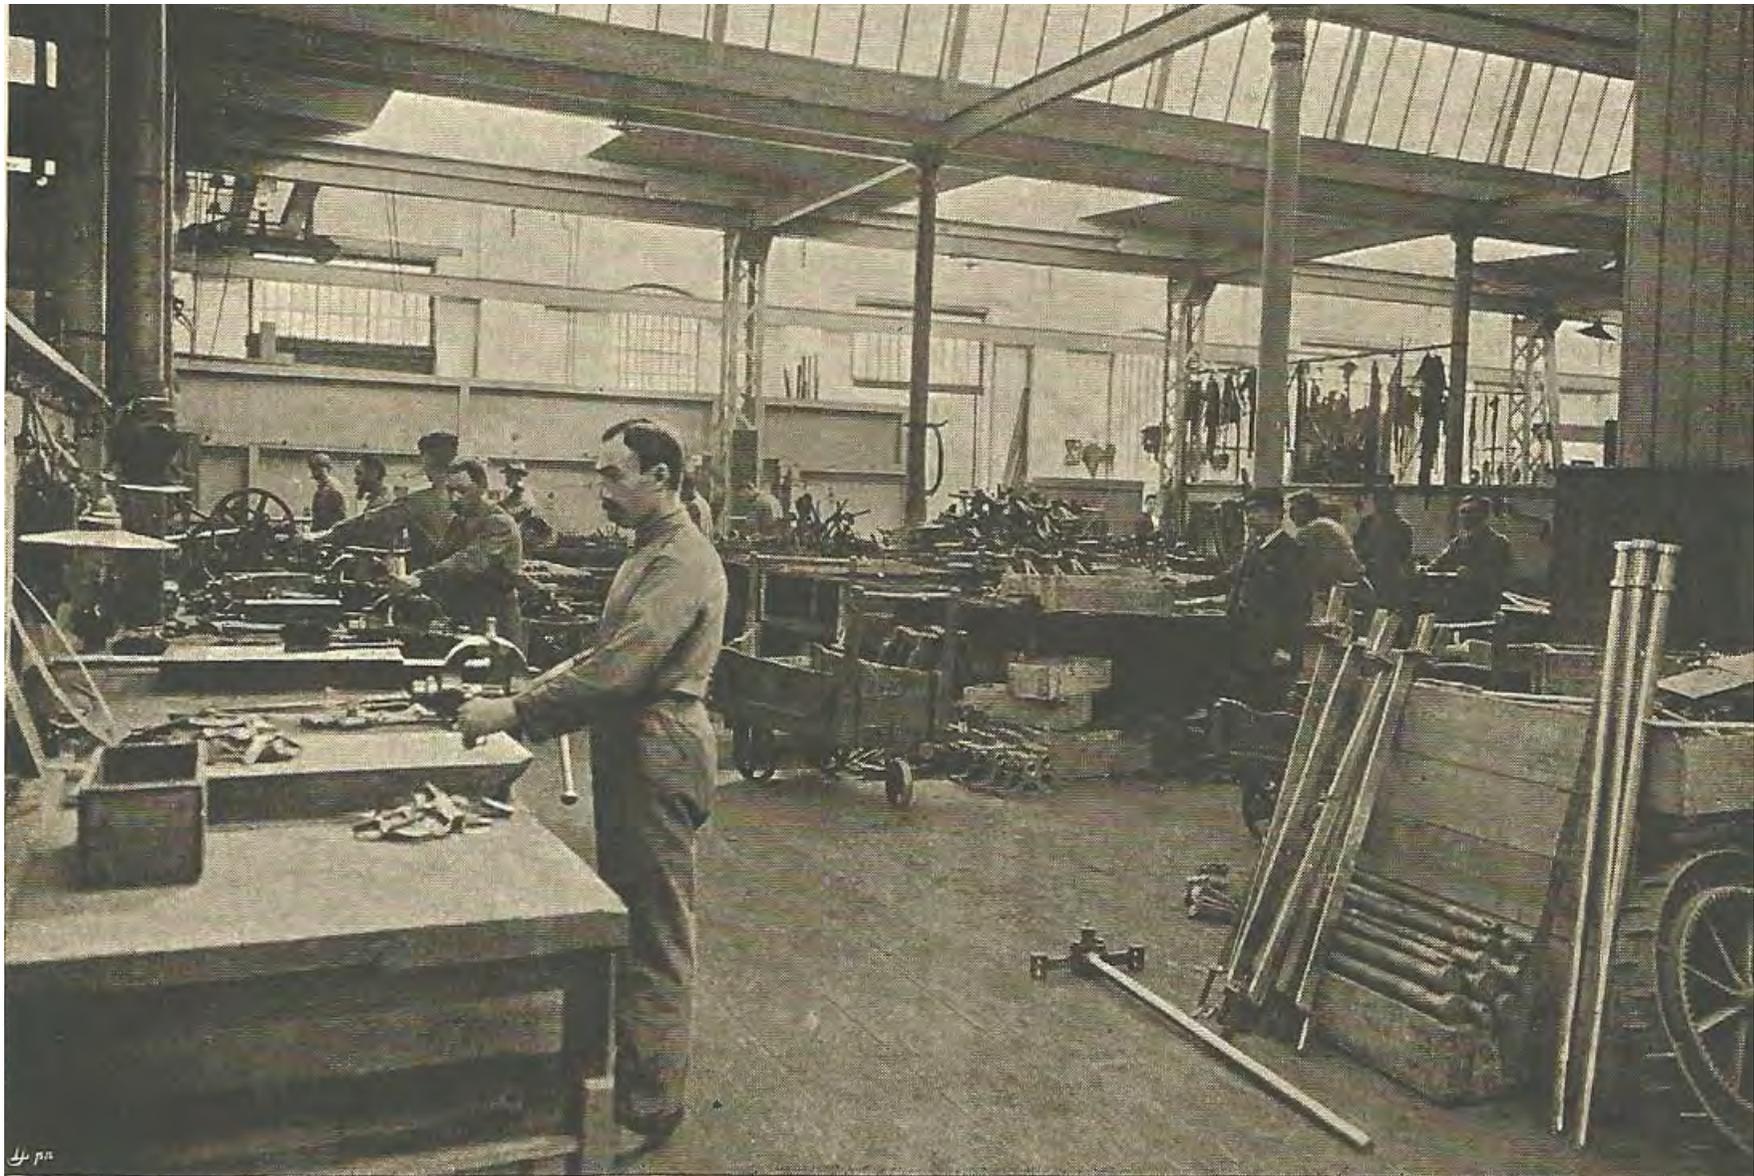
Appreturwerkstätte für Bestandteile zu Dreschmaschinen (VIII)
